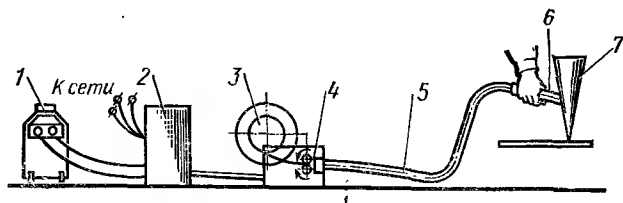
Схемы установки для полуавтоматической электрошлаковой сварки:
